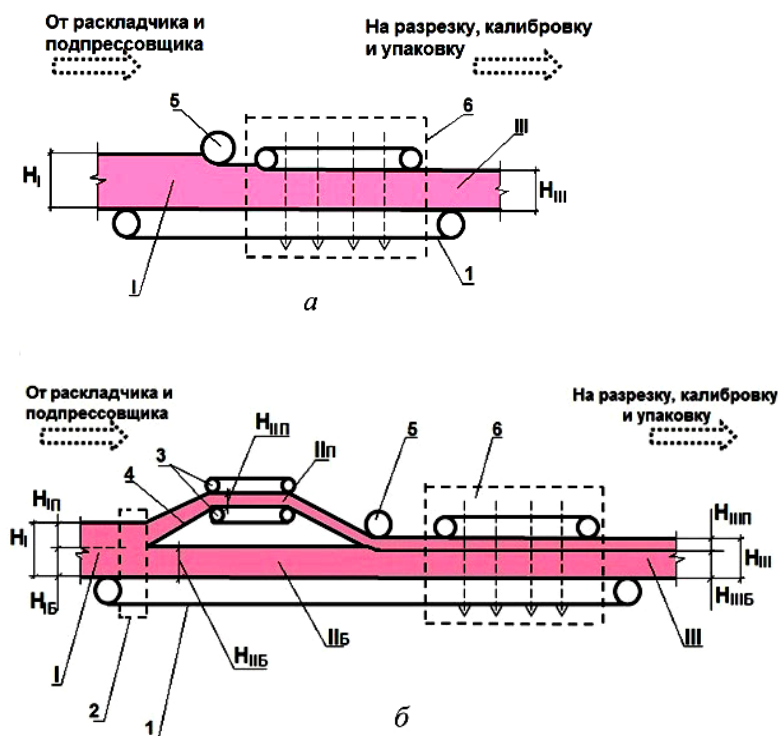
Схемы изготовления плит: а — равной плотности; б — двойной плотности: I — минераловатный ковер после раскладчика и подпрессовщика; II_п — покровный слой (в процессе подпрессовки); II_б — базовый слой после разрезки; III — минераловатный ковер с отвержденным связующим после камеры тепловой обработки; 1 — сетчатый конвейер; 2 — резательное устройство; 3 — уплотняющие конвейеры; 4 — направляющий стол; 5 — подпрессовочное устройство; 6 — камера тепловой обработки
